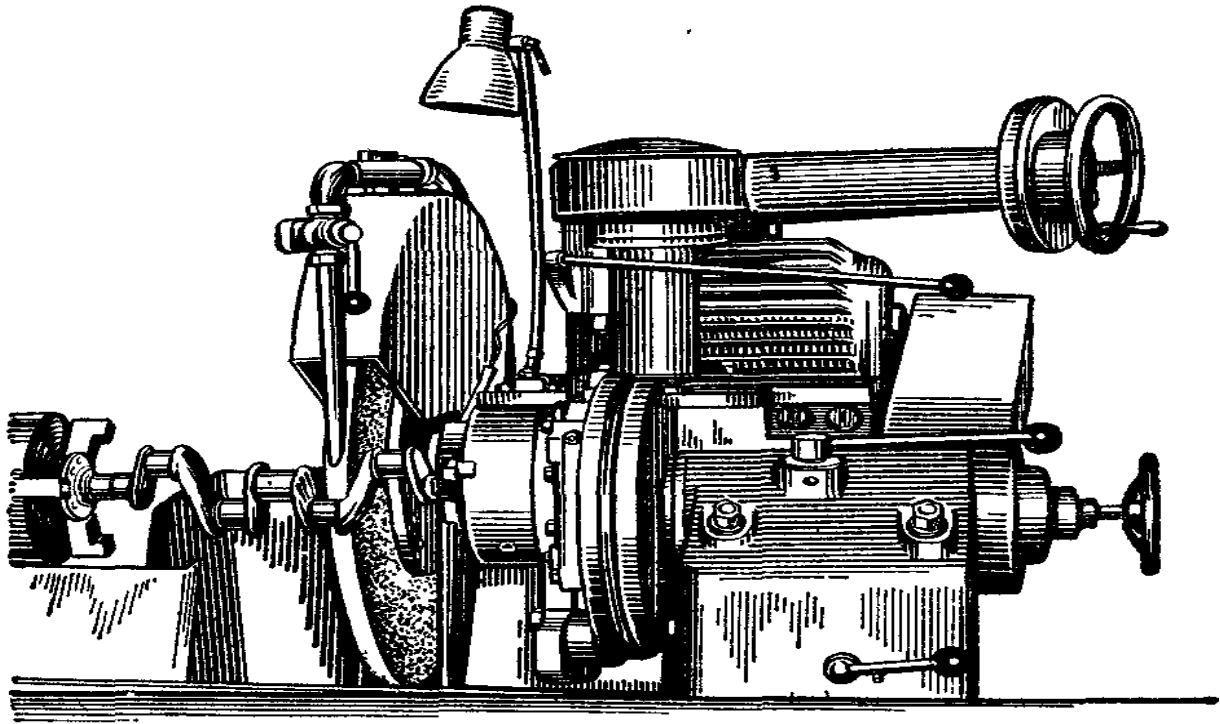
Шліфування шатунної шийки колінчастого вала на верстаті 3423
